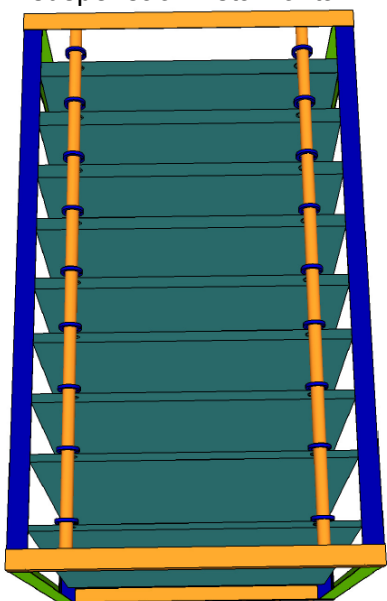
Estrutura metálica com sacos em suspensão. Vista de topo.
